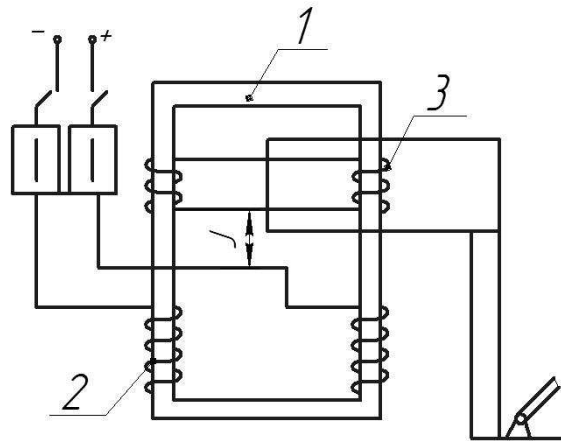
Конструктивная схема сварочного трансформатора
